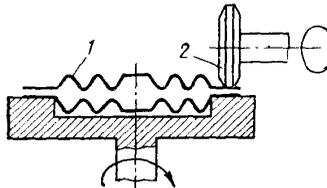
Контактная сварка мембранного чувствительного элемента
